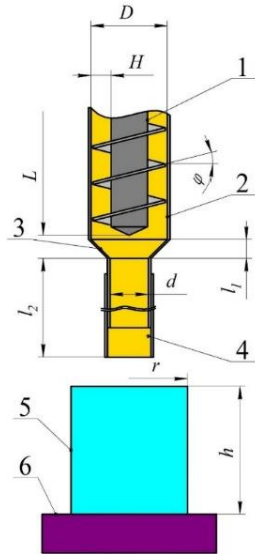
Схема дозатора із рухомим патрубком: 1 – шнек; 2 – корпус; 3 – конфузор; 4 – телескопічний патрубок; 5 – тара; 6 – зважуючий елемент
